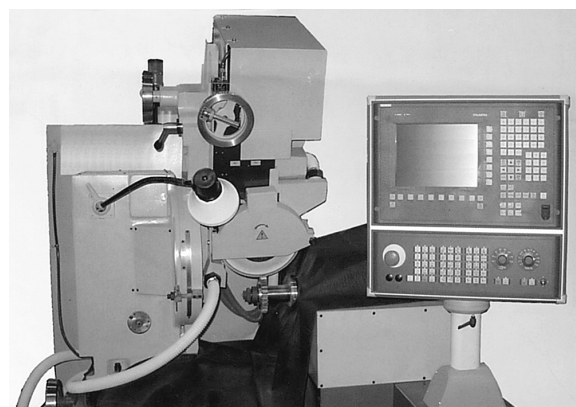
Зубошлифовальный станок МШ504С с ЧПУ
